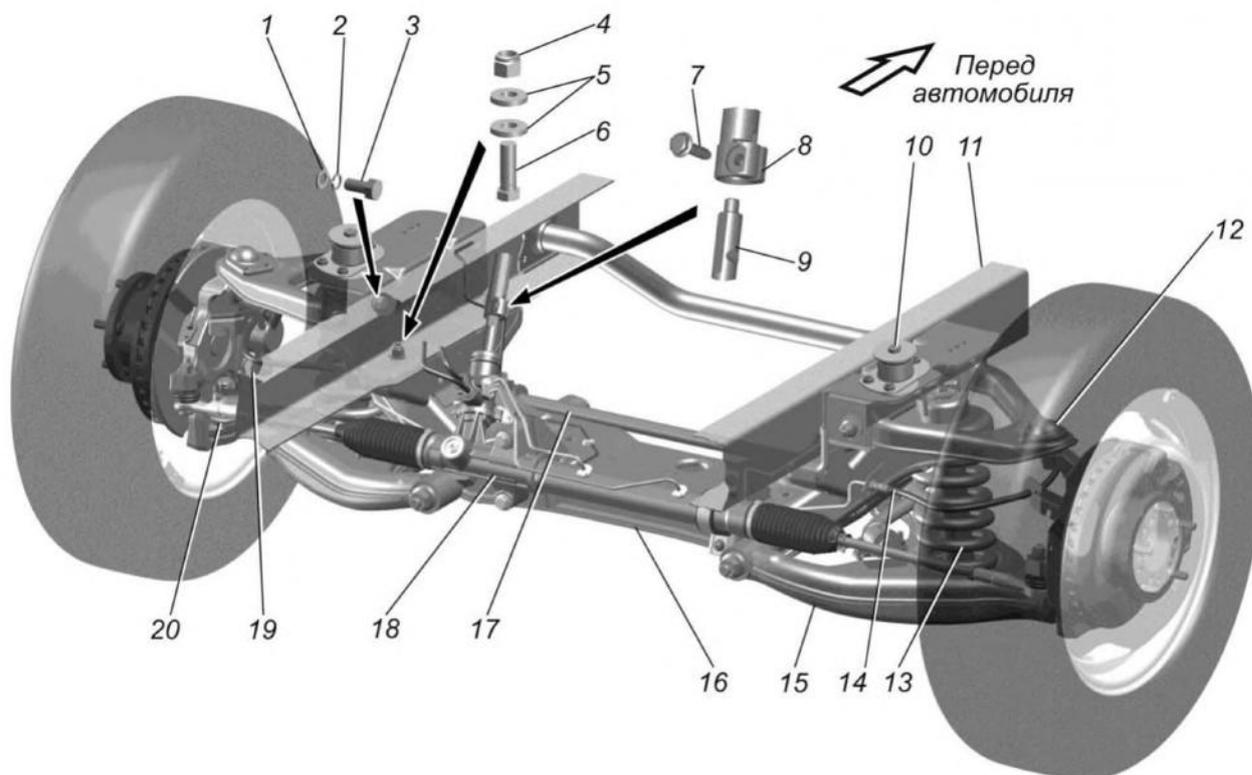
Установка передней подвески с рулевым механизмом: 1,2,5 – шайбы; 3,6,7 - болты; 4 – гайка; 8 – карданный вал рулевого управления; 9 - входной вал рулевого механизма; 10 – болт крепления передней опоры кузова; 11 – рама; 12 - шарнир шаровой верхней; 13 – пружина; 14- шланг передних тормозов; 15 – нижний рычаг; 16 – подрамник; 17 – стабилизатор поперечной устойчивости; 18 - рулевой механизм; 19 – болт крепления тормозной скобы; 20 - шарнир шаровой нижней
